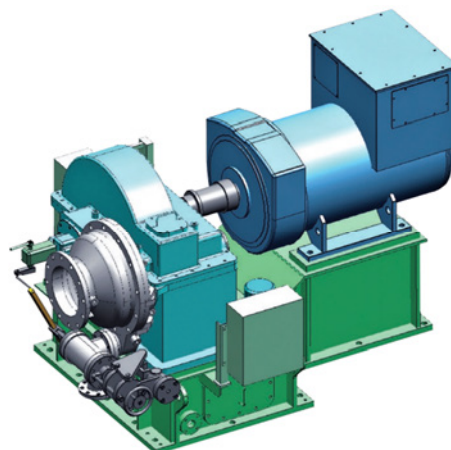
Turbína TGM Kanis Turbinen GmbH typu CT [16]
